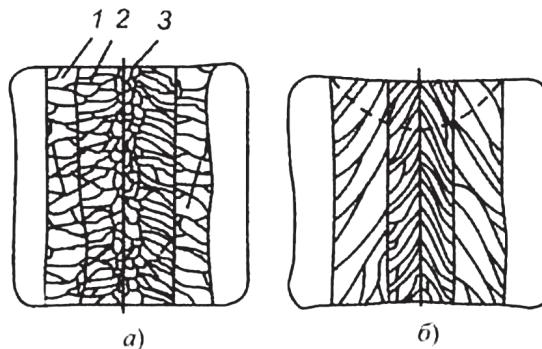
Строение металла шва при электрошлаковой сварке
